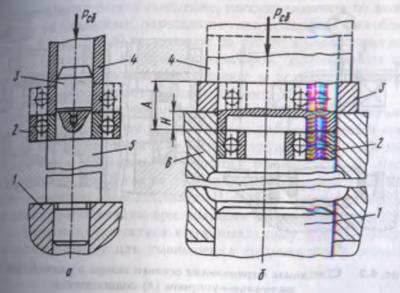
Схемы напрессовки подшипника на ва така (а) и запрессовки в корпус (б):
